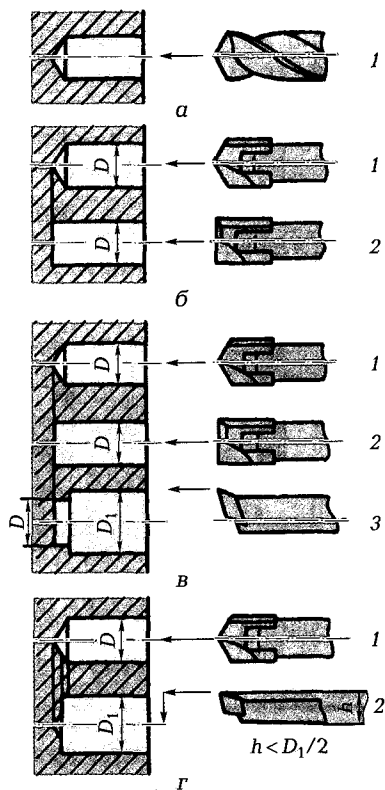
Инструменты для обработки внутренних основных зон:
